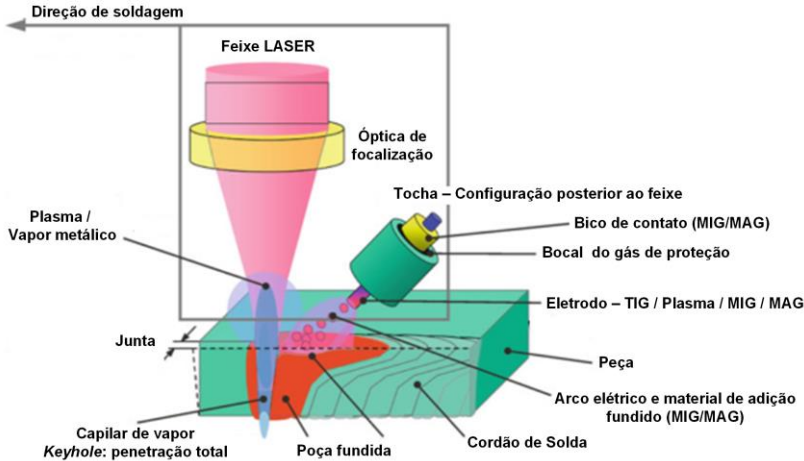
Princípio do processo de soldagem híbrida LASER-Arco (Adaptado de [1])
